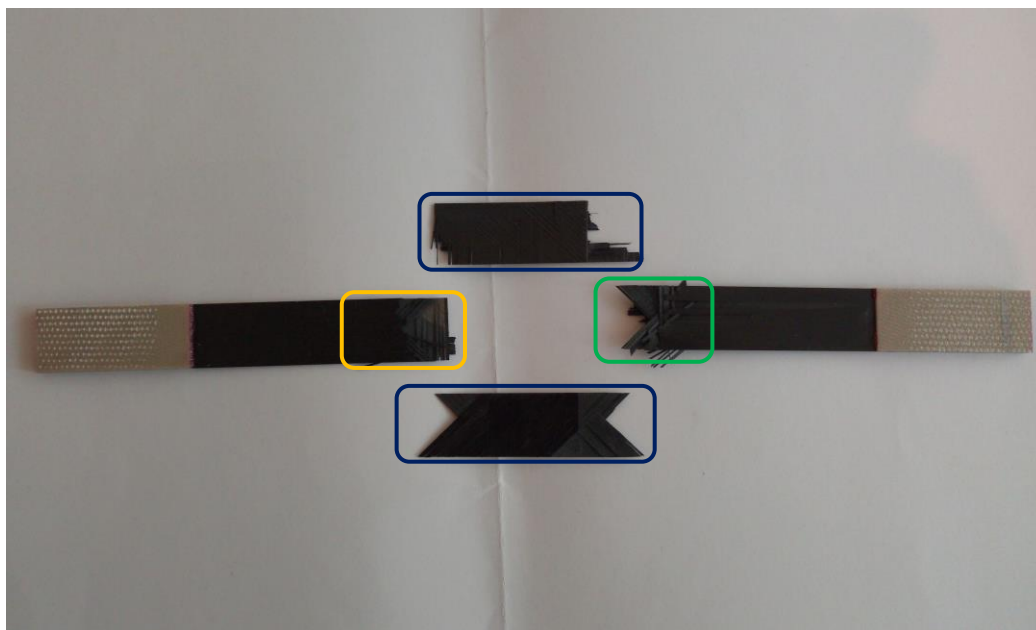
Detalle de las zonas de rotura de la probeta TS2
